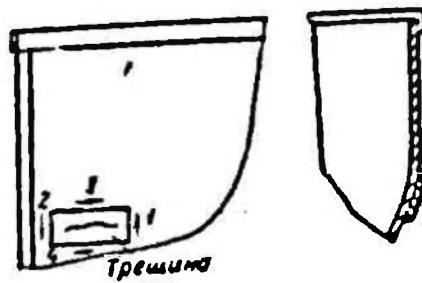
Очередность наложения швов и направление сварки трещины в кузове вагонетки
